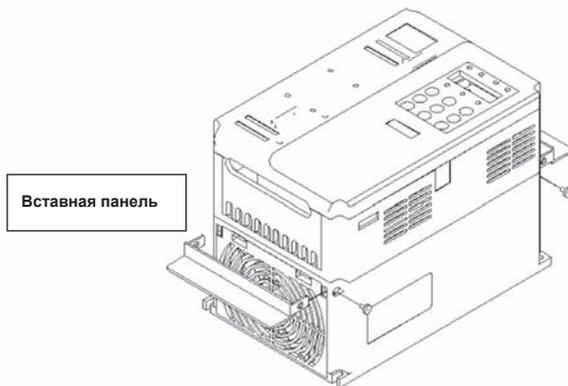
б Установка креплений для преобразователя в пластиковом корпусе
